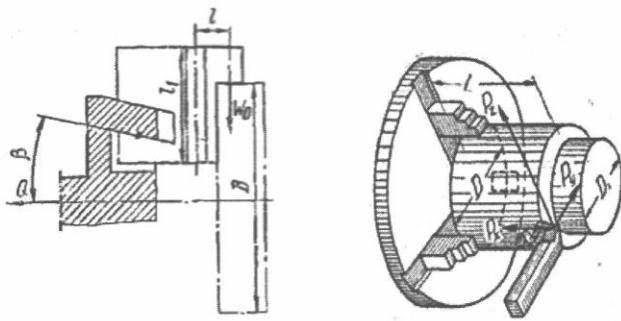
Схема расположения действующих сил при закреплении детали
